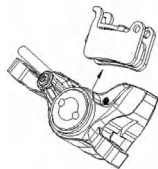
Démontage/montage des plaquettes de frein et des accessoires
